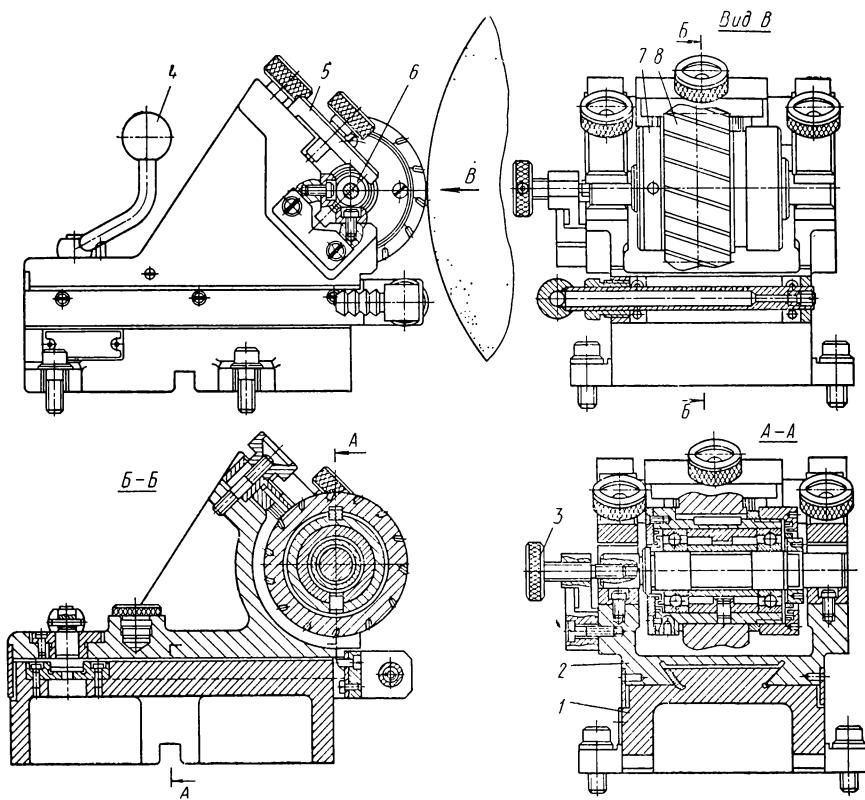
Приспособление для накатывания профиля круга роликом на резьбшлифовальном станке 5822
